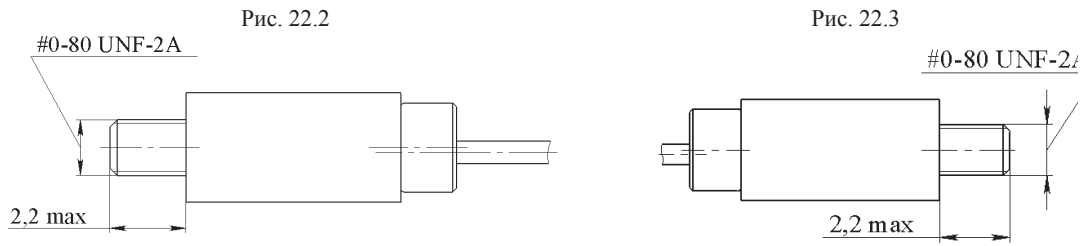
Соединитель СП450-08...1...ГГ2...
